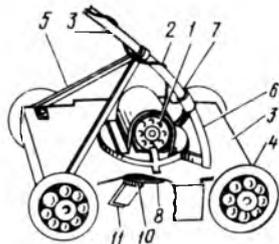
1 — электрополотер П-2; 2 — шнур питания (25...30 м); 3 — защитный кожух; 4 — колесо; 5 — опорный кронштейн; 6 — вилка; 7 — удлинитель рычага управления; 8 — рычаг управления; 9 — диск; 10 — прокладка; 11 — нож
